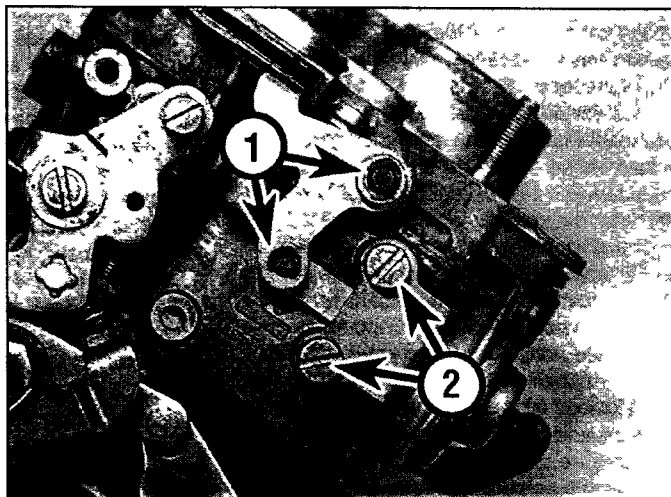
Снимите фиксаторы (1) и отсоедините поворотный рычаг вакуумного привода от крышки карбюратора
